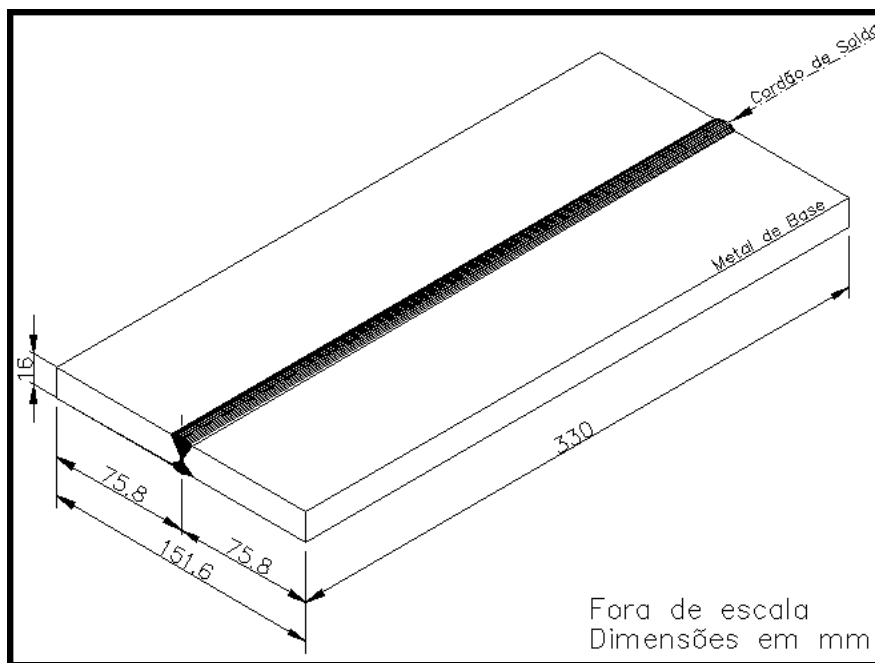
Desenho ilustrativo das dimensões da junta soldada.
